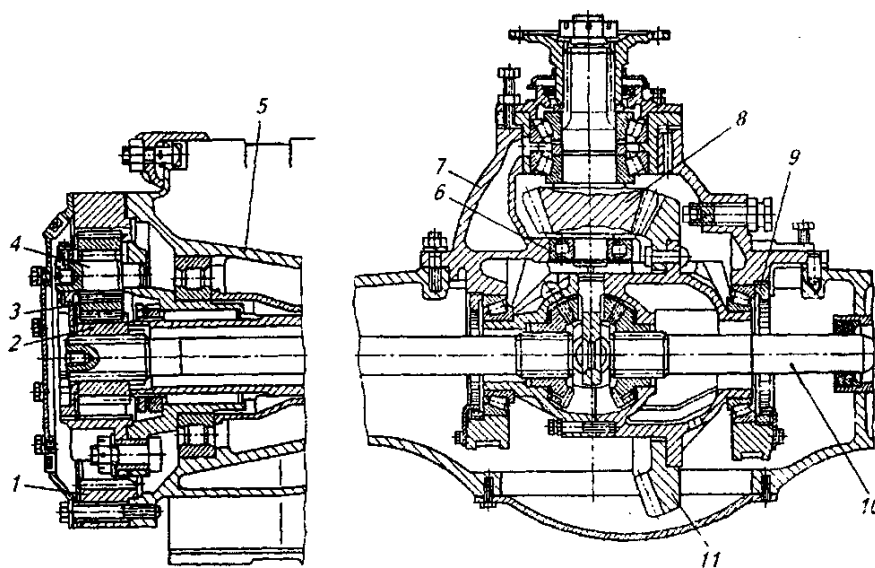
Двойная разнесенная главная передача: 1 — коронное колесо; 2 — солнечное зубчатое колесо; 3 — сателлит; 4 — ось сателлит; 5 — ступица колеса; 6 — дополнительная опора; 7 — корпус главной передачи; 8 — ведущая шестерня главной передачи; 9 — регулировочная гайка; 10 — полуось; 11 — ведомая шестерня главной передачи
